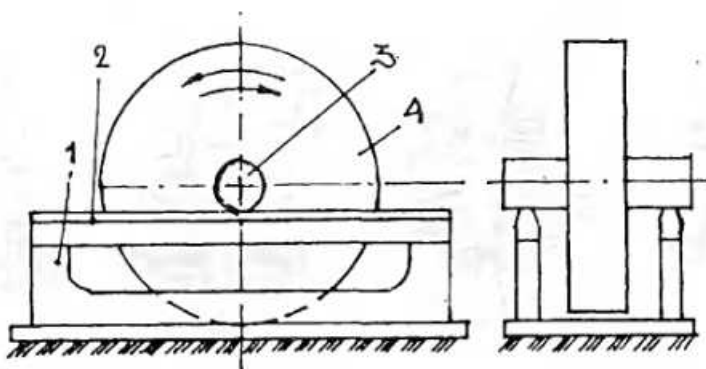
Схема балансувального верстата: 1 - станина; 2 - призма; 3 - вал; 4 - робоче колесо
